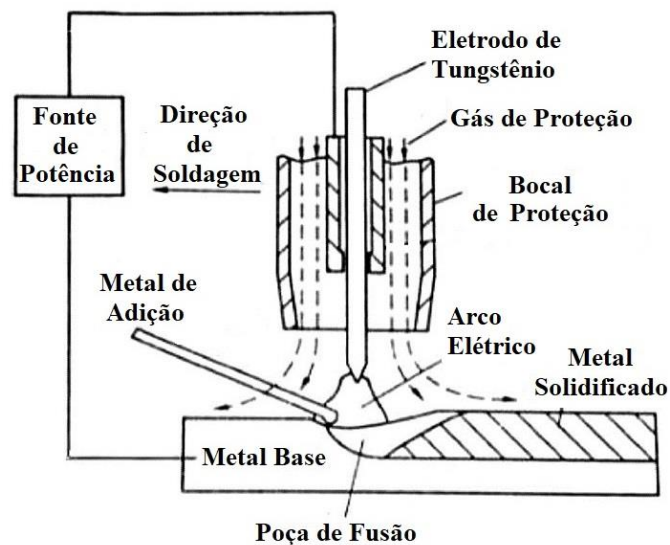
Esquema do processo de soldagem TIG [Wang, 2014].
